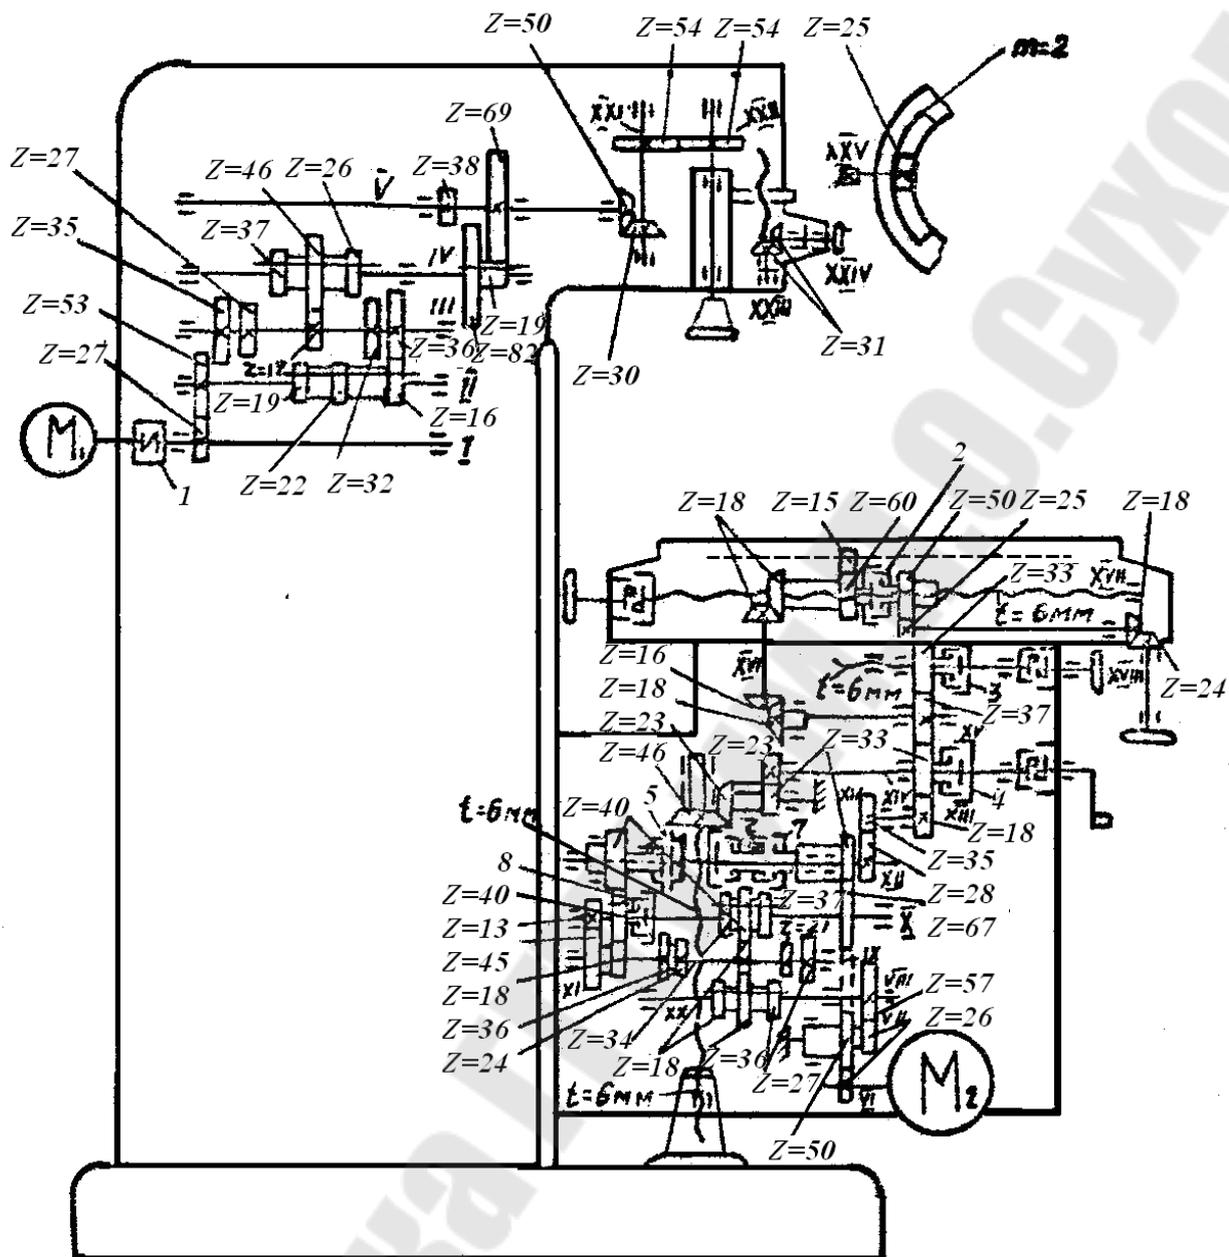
Кинематическая схема вертикально-фрезерного консольного станка
